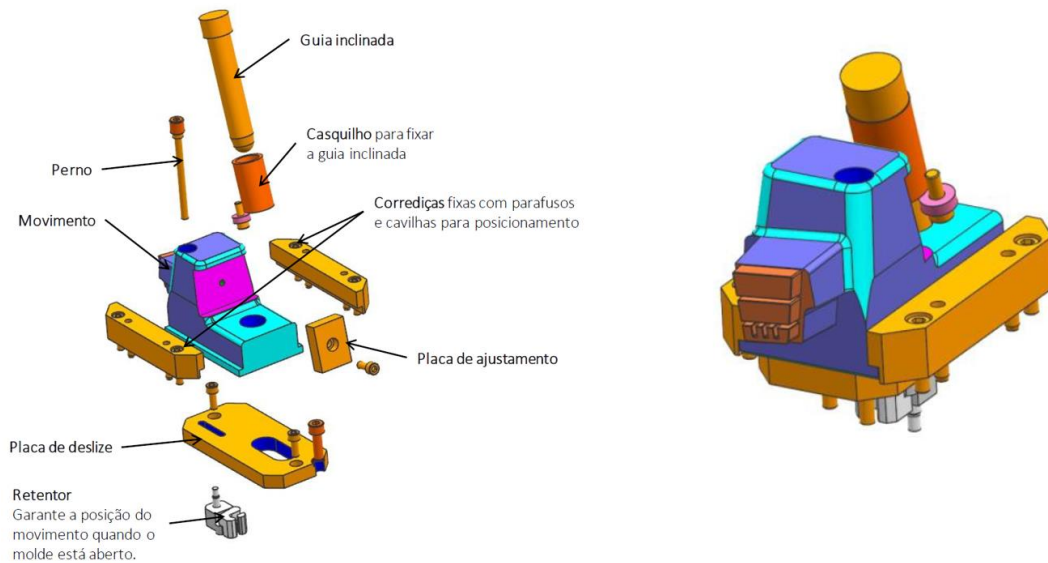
Vista explodida do movimento mecnico,  esquerda, e movimento mecnico,  direita (Marques, 2021).
